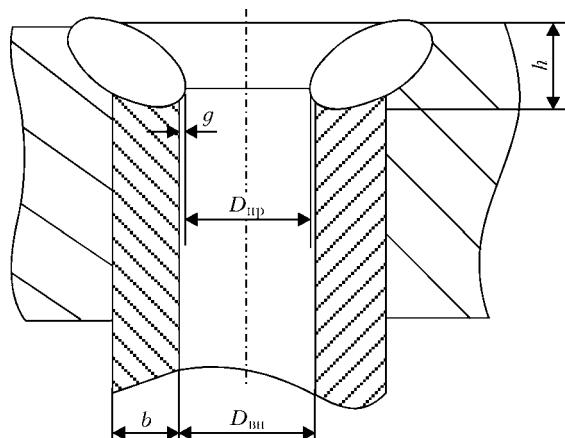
Схема сварного соединения трубы-трубная решетка:  $h$  — высота рабочего сечения шва;  $g$  — величина наплыva шва;  $b$  — толщина стенки трубы;  $D_{\text{ин}}$  — внутренний диаметр трубы;  $D_{\text{пп}}$  — диаметр проходного сечения трубы
